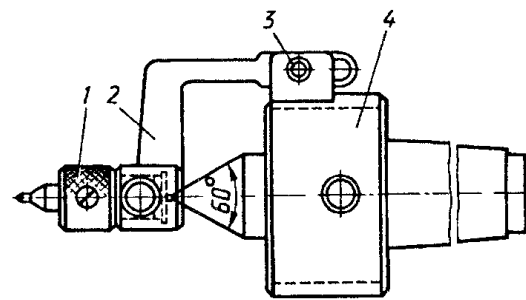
Пристрій з відкидним центрувальним свердлом до обертового центру: 1 – патрон; 2 – відкидна серга; 3 – вісь серги; 4 – обертовий центр
